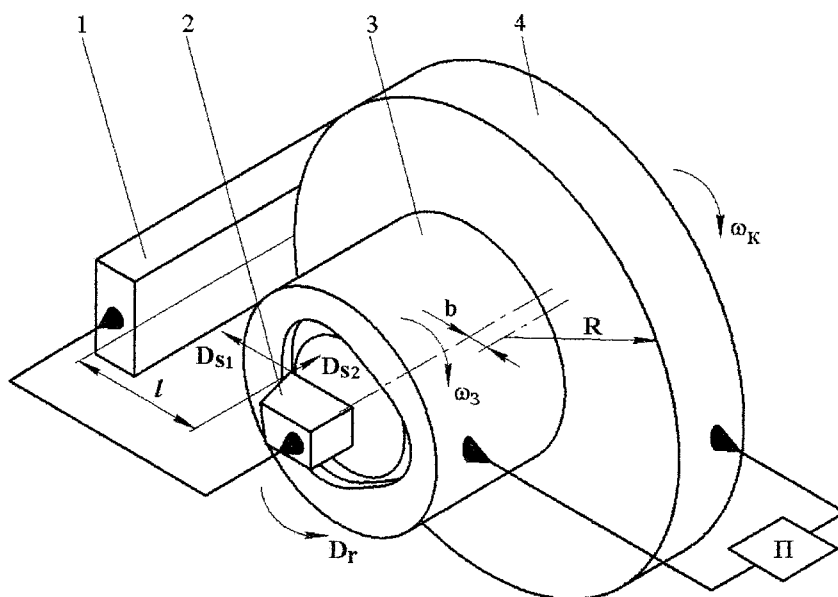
Схема обработки: 1 – шуп, 2 – резец, 3 – заготовка, 4 – копир
